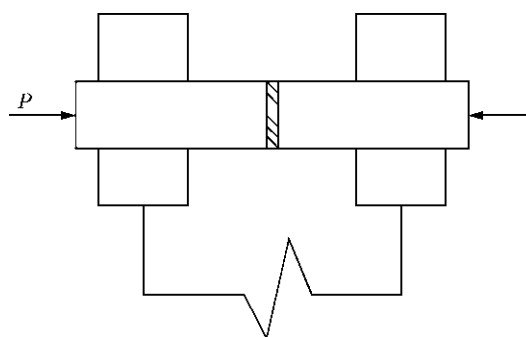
Схема контактной стыковой сварки сопротивлением интерметаллидного сплава Ti–47Al–1,5Cr–2Nb с использованием фольги (заштрихованная часть)
